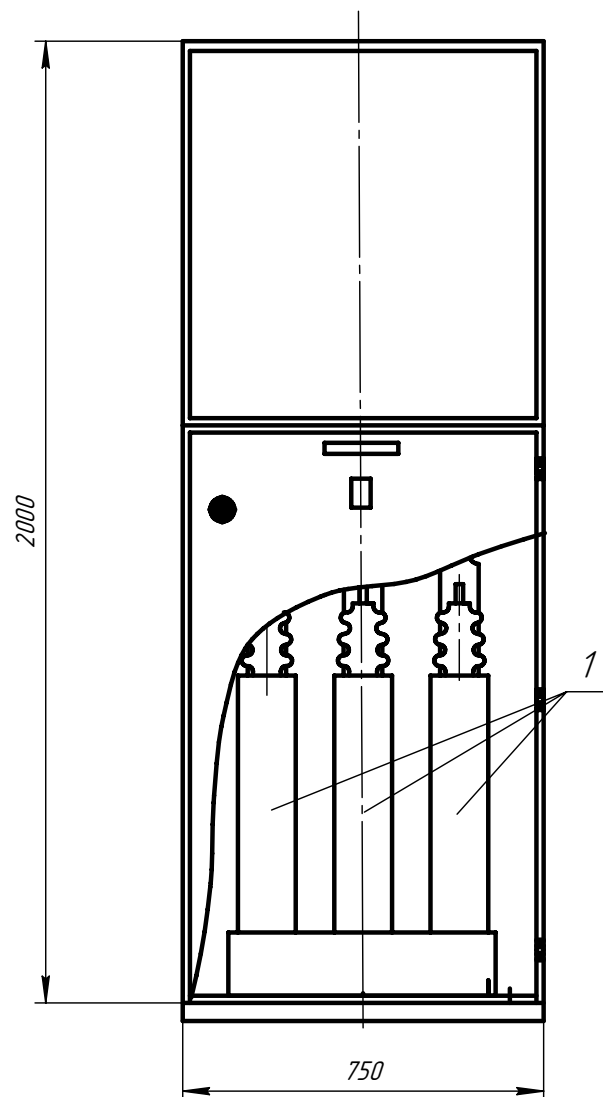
Габаритные, установочные, присоединительные размеры шкафов.
